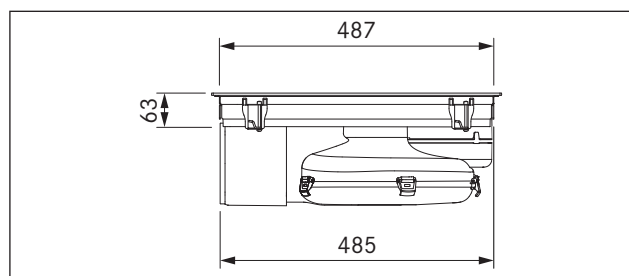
PUXU dimensioni apparecchio visto laterale
